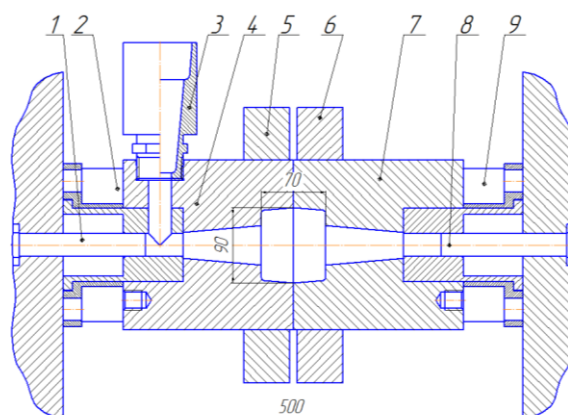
Чертеж технологической оснастки для производства заготовок поршей ДВС
